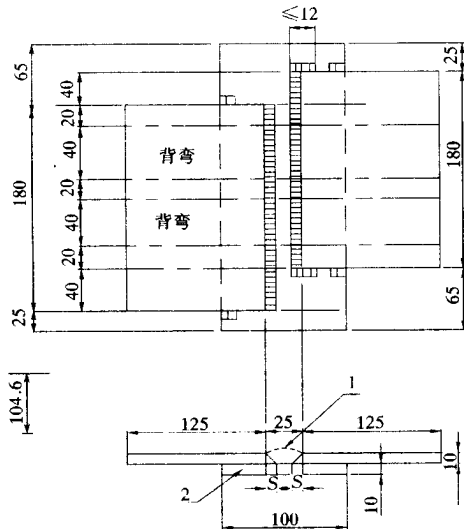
搭接角焊缝试件形式、尺寸和试样取样位置示意
